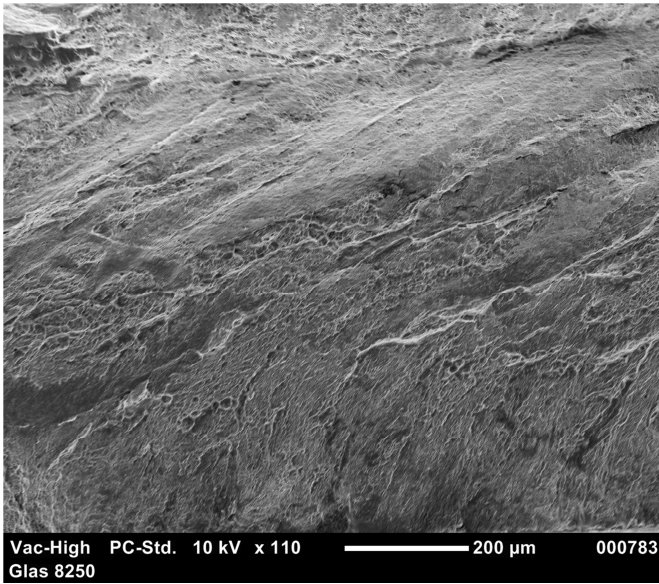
Fraktographische Detailaufnahmen der FSW-Verbindung ISF-33-00032
